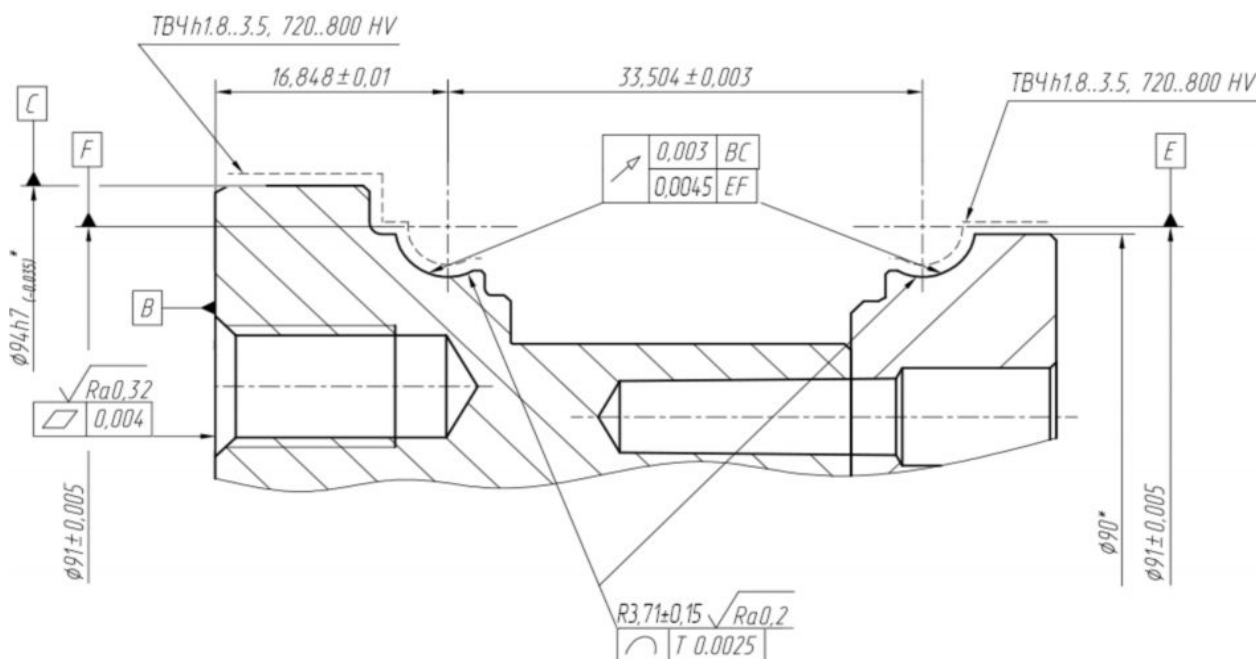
Фрагмент чертежа сборочной единицы «Фланец»
